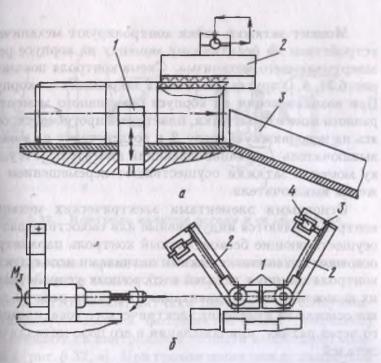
Контроль резьбы (а) и момента затяжки гайки (б)
